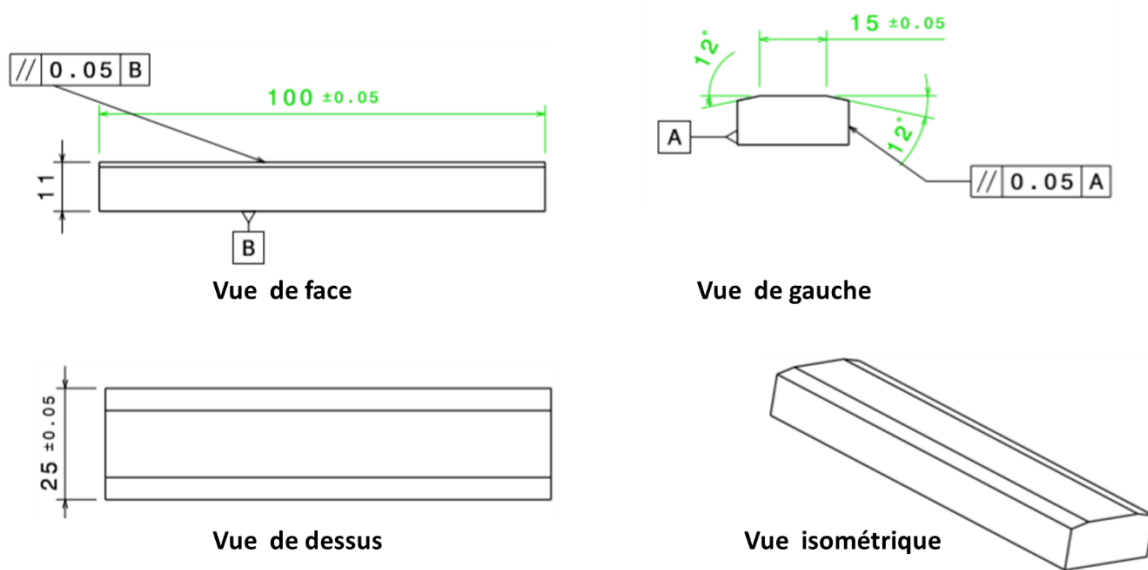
Dimensions 3D des éprouvettes de fatigue
